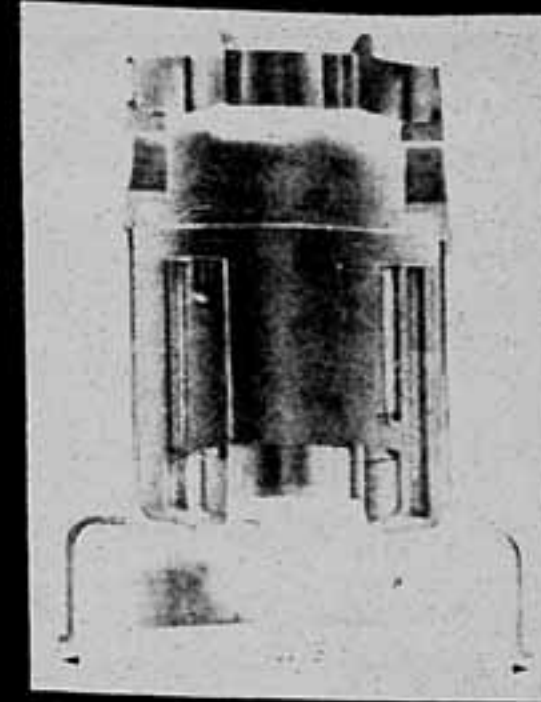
Motorgehäuse und Lagerschild für Staubsauger. Die beiden seitlichen Bohrungen des Lagerschildes sind mit einer Rudge-Verzahnung versehen.
